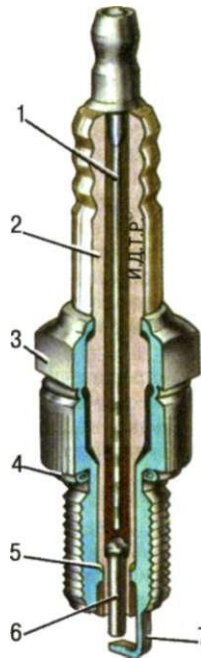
Устройство свечи зажигания: 1 - контактный стержень; 2 - изолятор; 3 - корпус свечи зажигания; 4 - уплотнительное кольцо; 5 - теплоотводящая шайба; 6 - центральный электрод; 7 - боковой электрод
